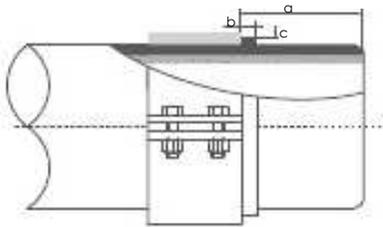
Dimensiones de la soldadura para junta TF auto anclada
